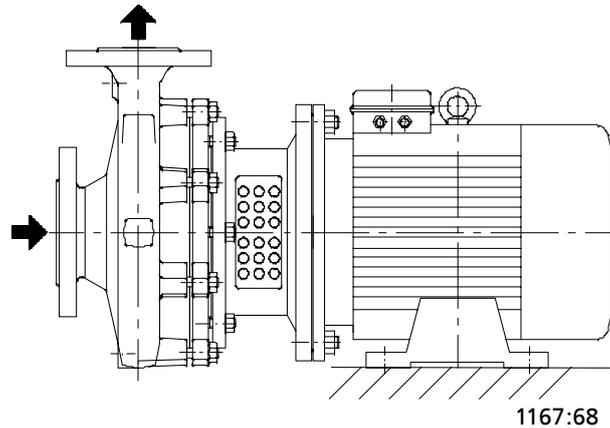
Motorfuß Befestigung unten, Motorgröße 132 = 5,5 kW bis 225 = 45 kW
